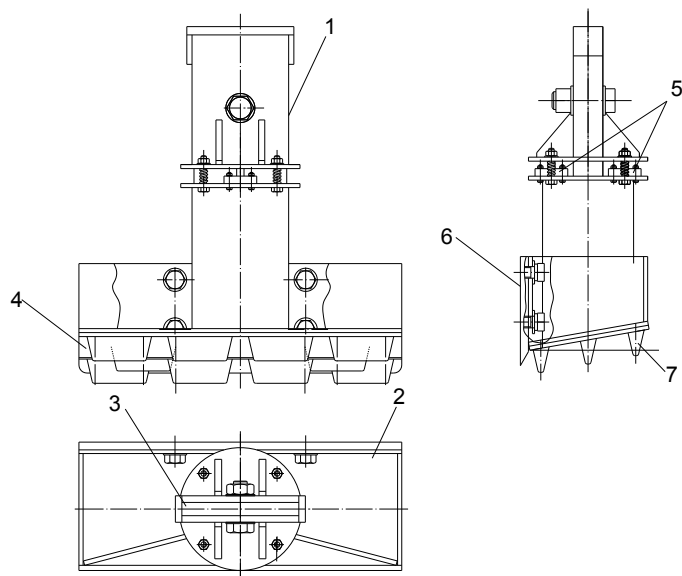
Корпус подпрессовки и дегазации анодной массы
